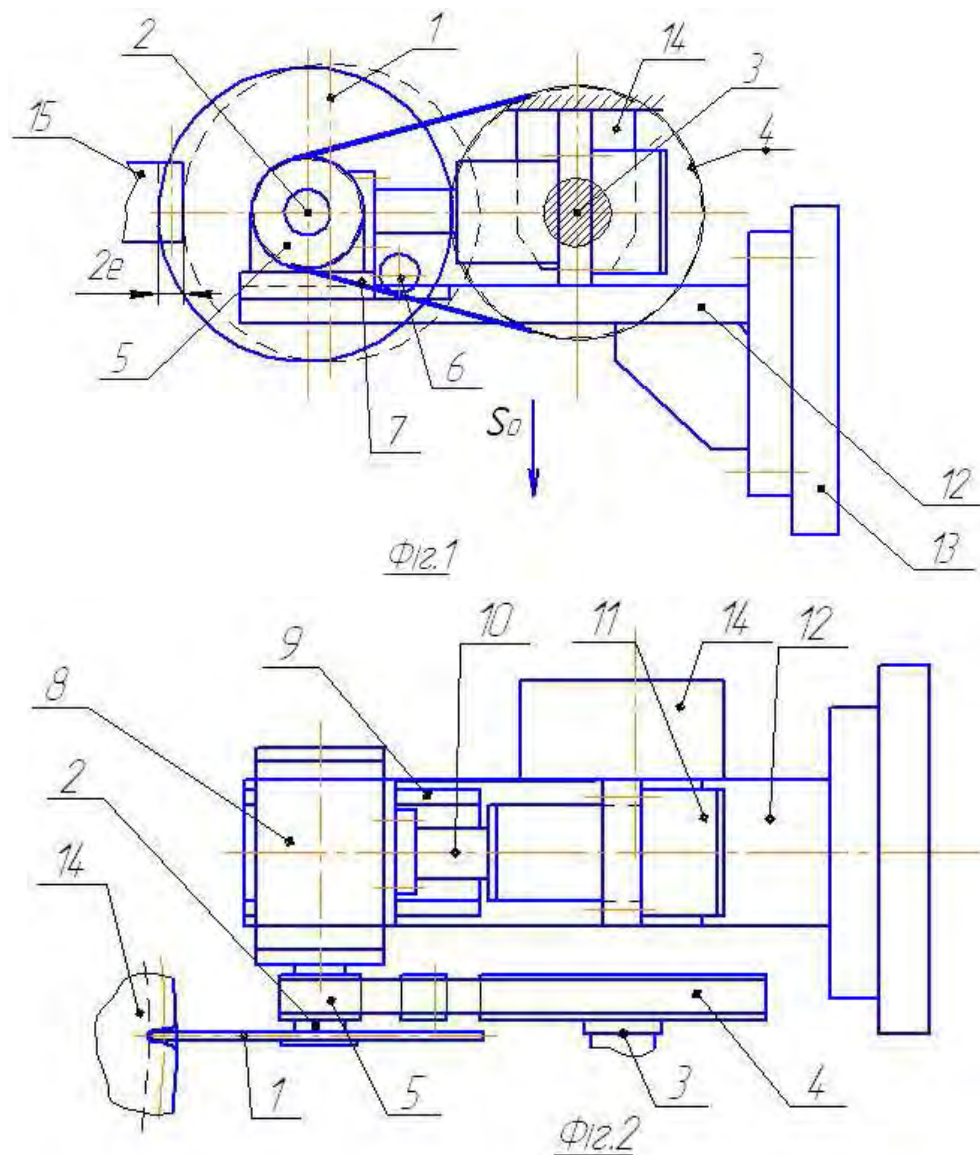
Робоча ділянка зубофрезерного верстата з приводами головного руху від інструментального шпинделя та переміщення каретки від серводвигуна
